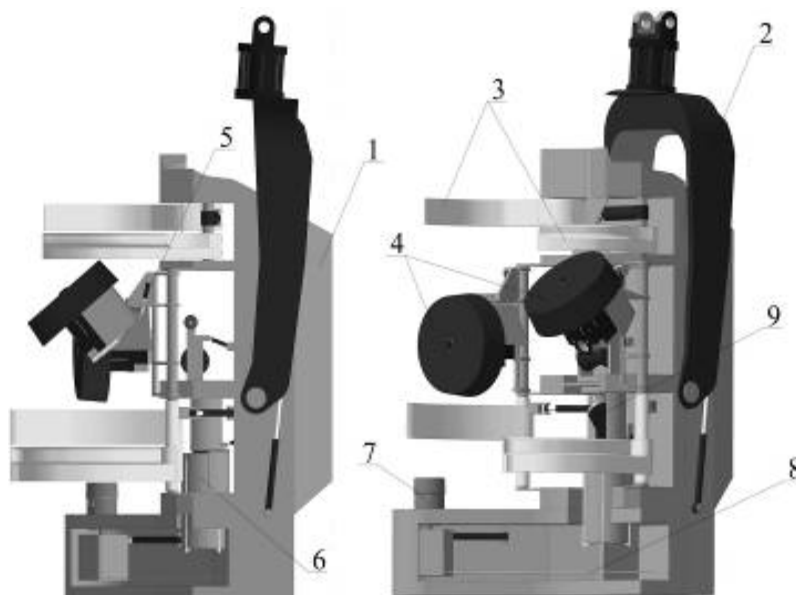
Принципиальная схема харвестерной головки с устройством для оцилиндровки сортиментов: 1 – корпус харвестерной головки; 2 – серьга с ротатором; 3 – сучкорезные ножи; 4 – поворотные протаскивающие вальцы; 5 – гидроцилиндр поворота протаскивающих вальцов; 6 – фреза для оцилиндровки закомелистости; 7 – гидромотор привода пилы; 8 – пила; 9 – гидромотор привода фрезы.
